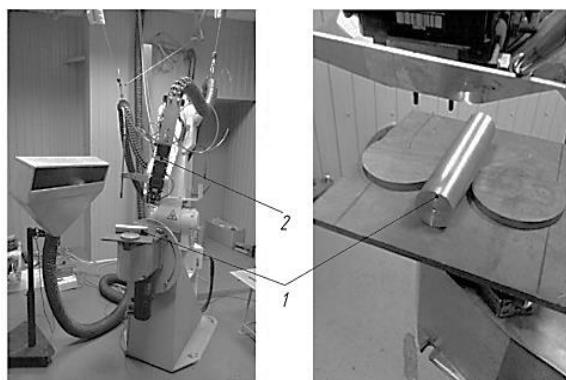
Лазерная установка ЛС-5, где 1 – заготовка; 2 – лазерная оптическая головка
